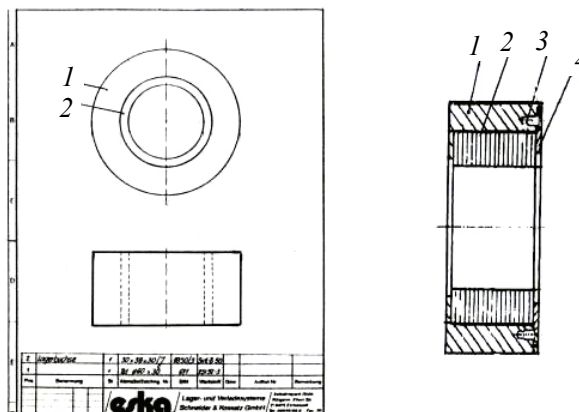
Самосмазывающийся подшипник скольжения для подъемника фирмы «ESKA»: 1 – корпус; 2 – деревянная втулка торцового гнущья; 3 – винт; 4 – крышка
